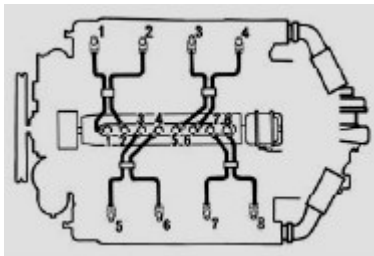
Схема соединения топливопроводами высокого давления секций ТНВД и форсунок цилиндров двигателя ЯМЗ-238
